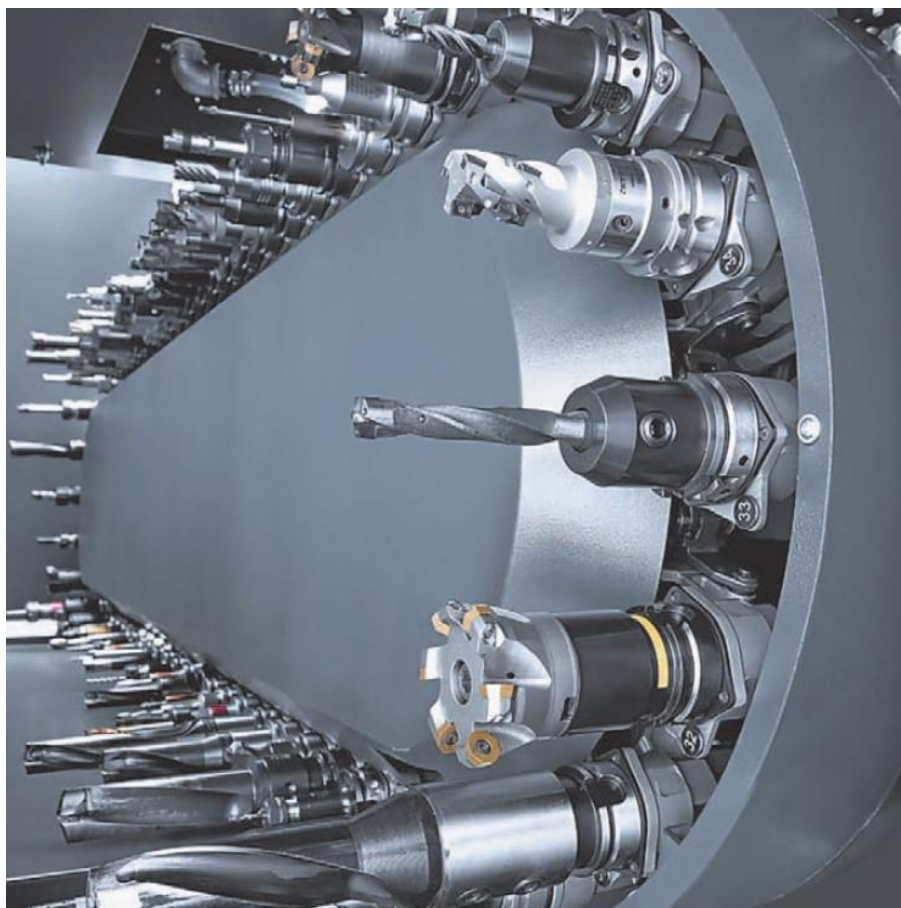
Інноваційне обладнання для виготовлення деталей
